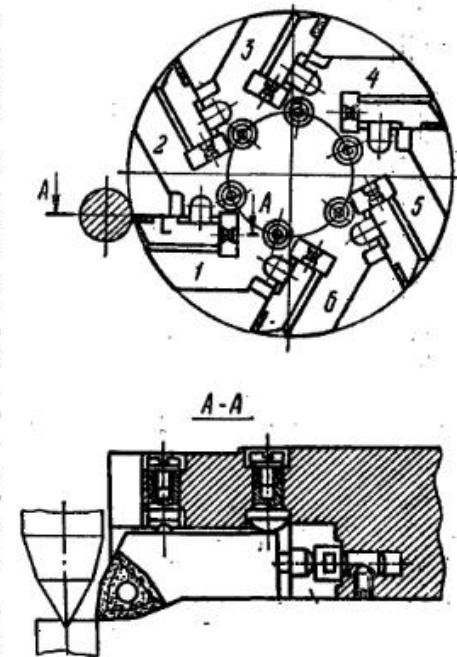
6-позиционный резцедержатель станка 16К20ХЗС4
